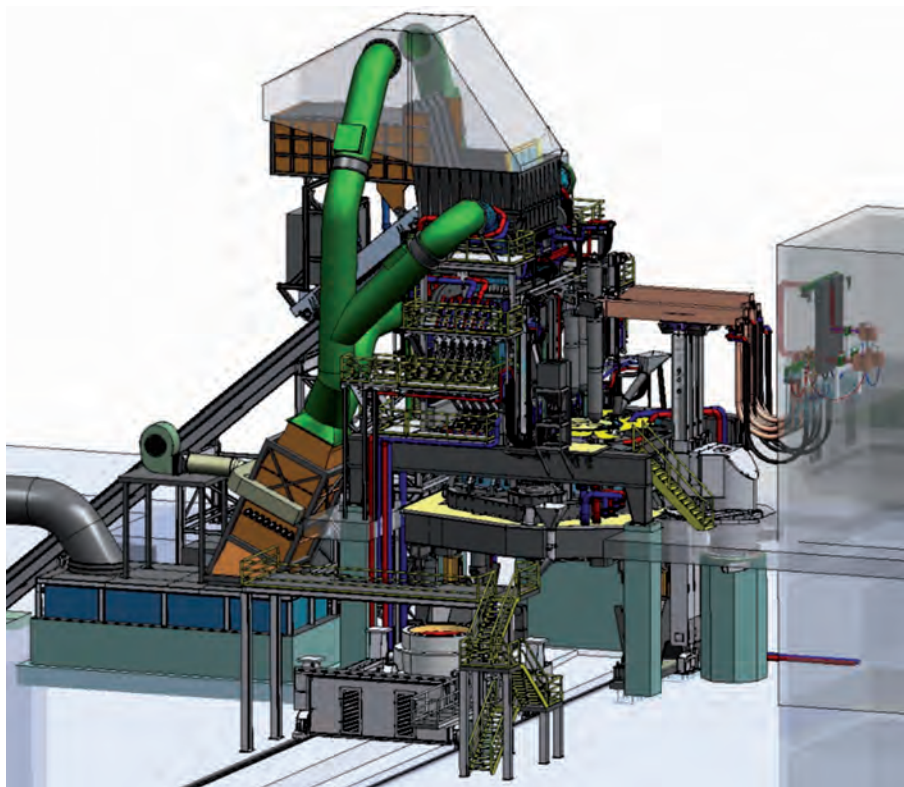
Общий вид ДСП Quantum со стороны выпуска
